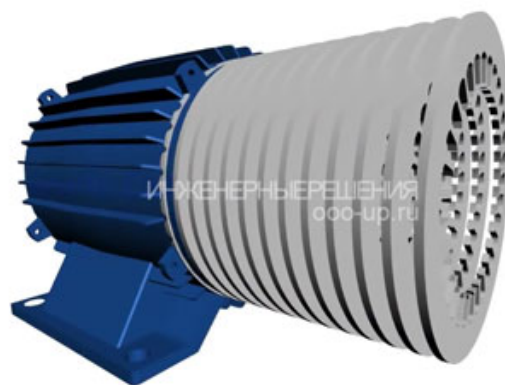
Конструкция шихтованного сердечника асинхронного двигателя
